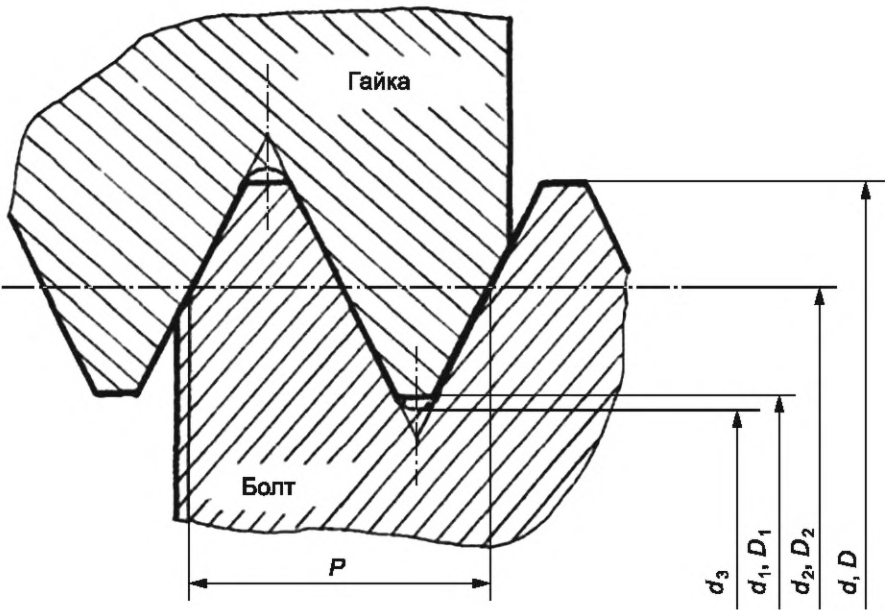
Профиль метрической резьбы с обозначением его элементов
